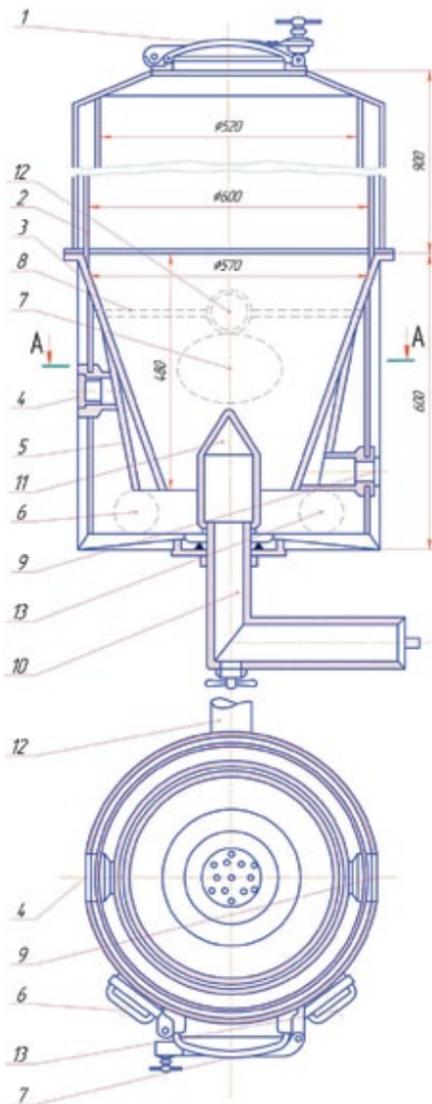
Схема газогенераторной установки «Г. О. Д. Г» (Германия): 1 – крышка; 2 – бункер; 3 – топливник; 4 – патрубок; 5 – кожух; 6, 7 – люки; 8 – кольцо угловое; 9 – второй патрубок; 10 – труба; 11 – сопло; 12 – газоотводный патрубок; 13 – люк
